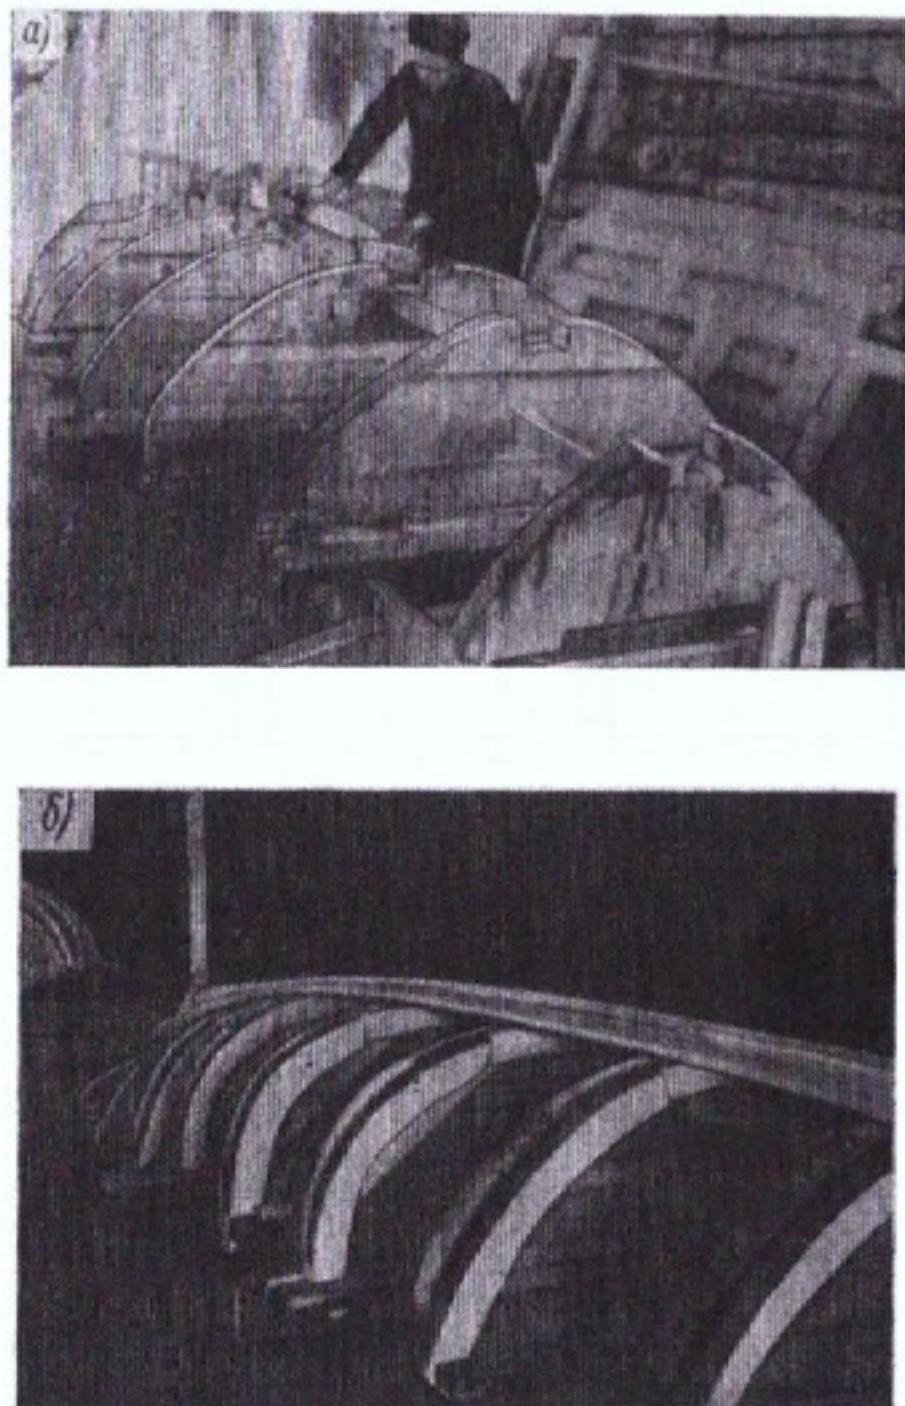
Простейший тип стапель-кондуктора: *а* — общий вид стапеля; *б* — выставка закладки и первый пояс обшивки.
